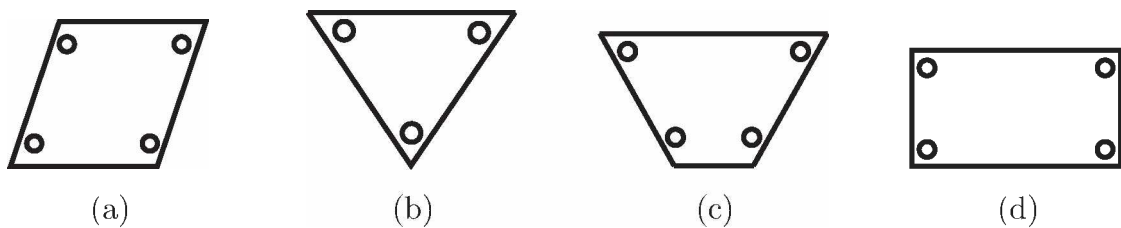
Geometrievarianten der Zwischenplatte: (a) rhombusförmige Platte für seitliche Bedienung; (b) Dreiecksform; (c) Trapezform; (d) rechteckige Geometrie der Platte für die Bedienung von oben.
